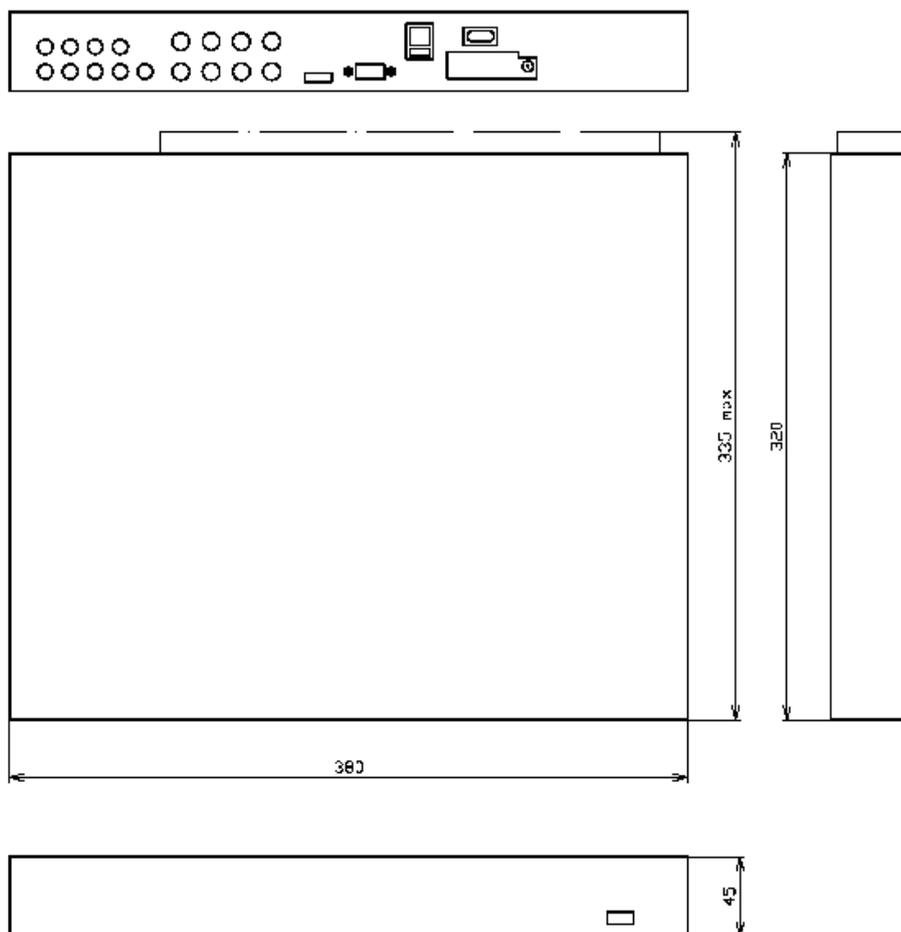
Габаритный чертеж ИВМ-8008.
